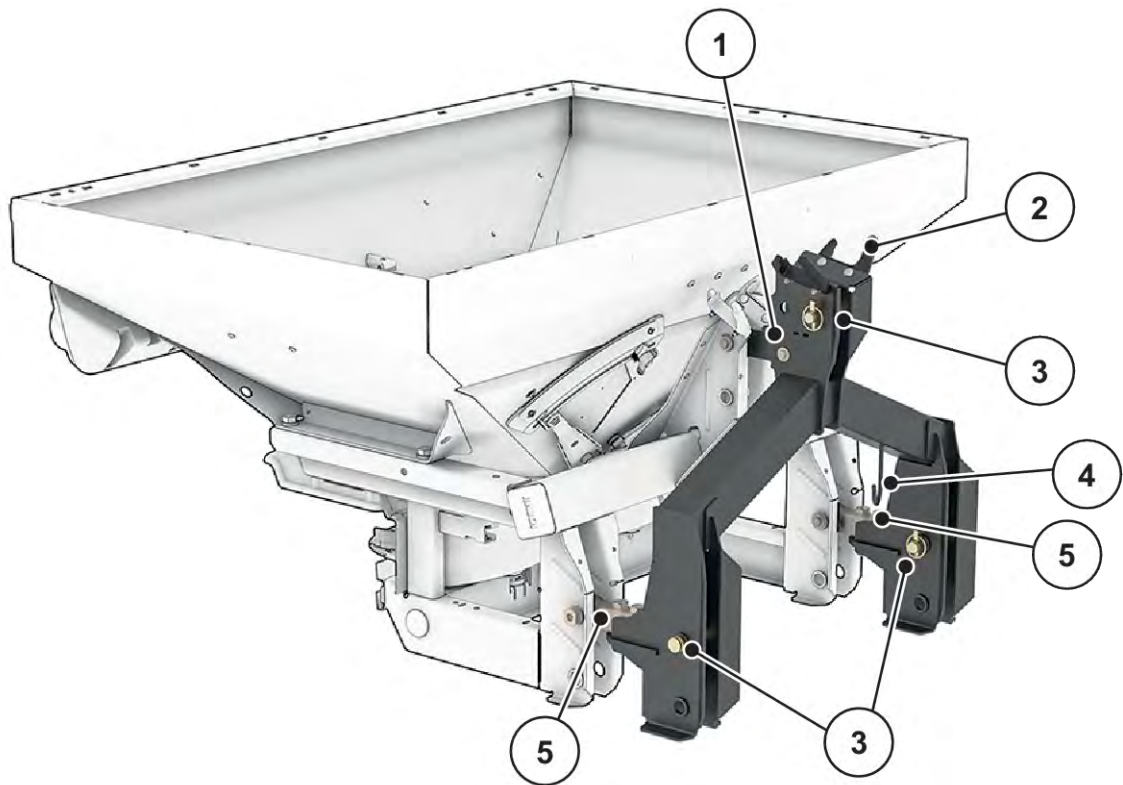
Огляд конструкційних вузлів. Передня частина з рамою ваг
